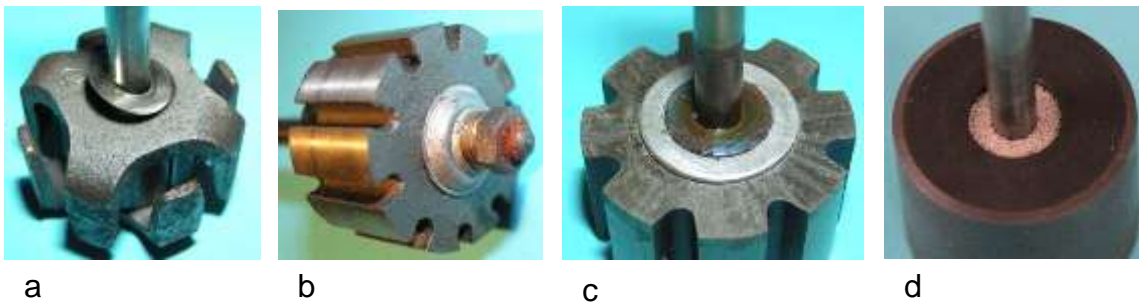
Polräder: a) Achtpoliges Klauenpolrad mit axial magnetisierten zweipoligen Magneten, b) Sternmagnet mit der Welle verschraubt, c) Sternmagnet mit der Welle verpresst, d) Keramisches Polrad mit der Welle vergossen
